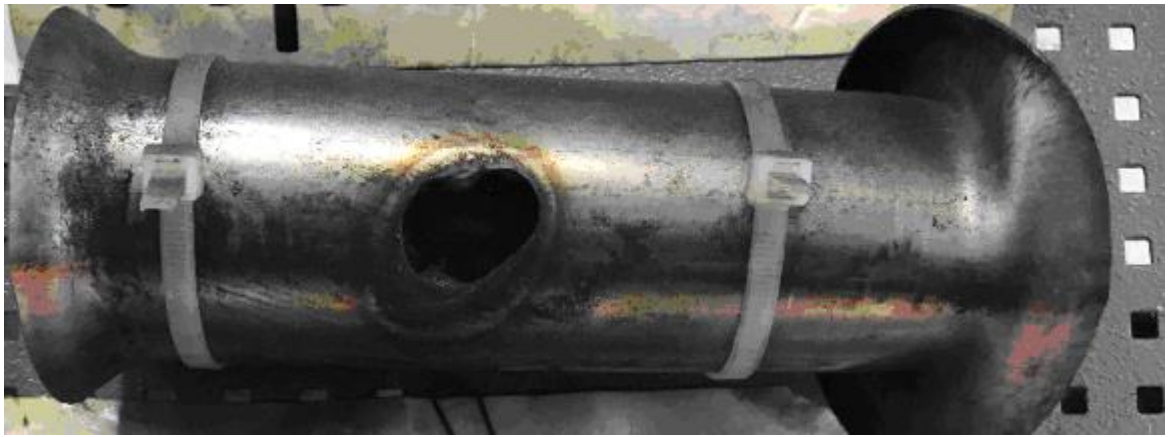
Дефекты при запуске линии сварки
